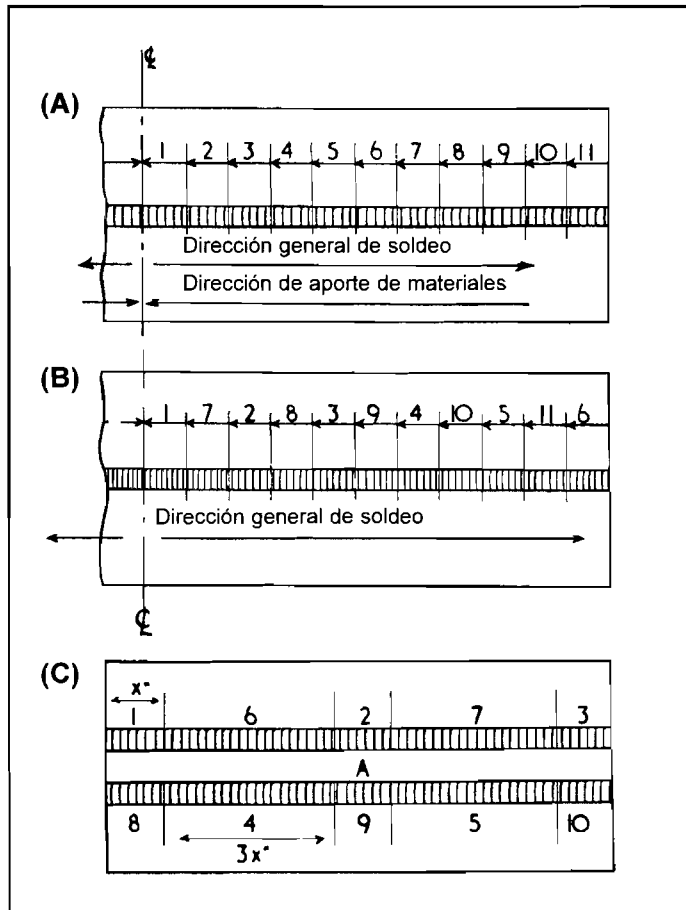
(A) SOLDEO DE PASO DE PEREGRINO. (B) SOLDEO A SALTOS. (C) TÉCNICA PARA REALIZAR DOS SOLDADURAS EN ÁNGULO EN FORMA DE T
